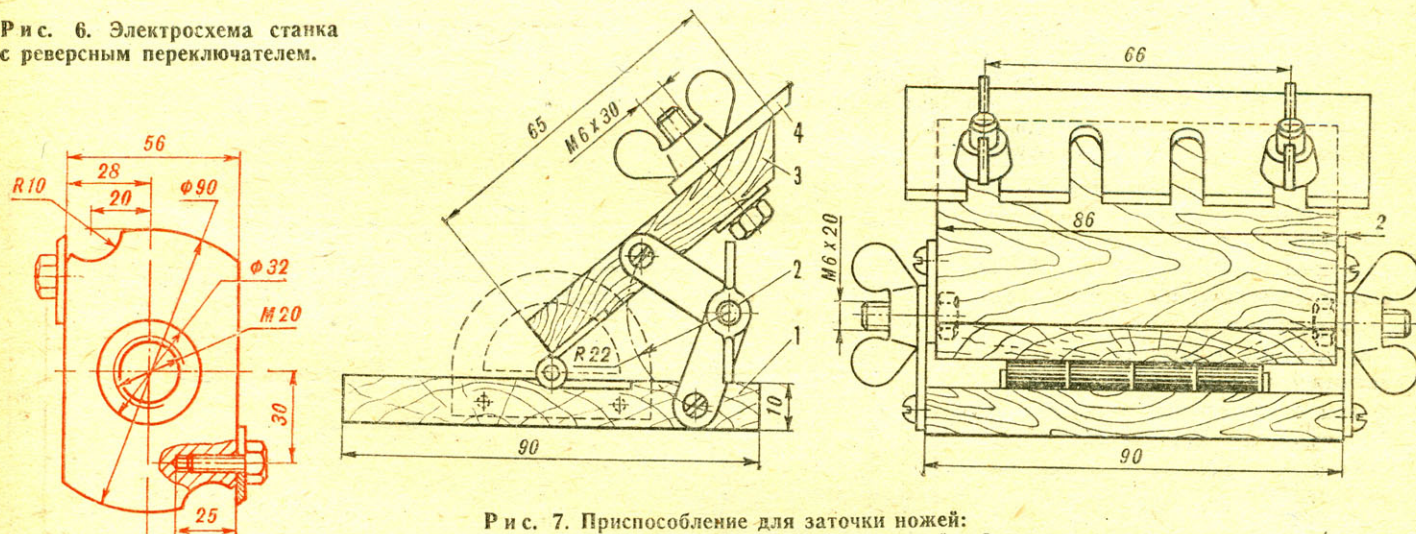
Приспособление для заточки ножей: 1 — основание, 2 — шарнирный кронштейн, 3 — планка крепления ножа, 4 — нож.
